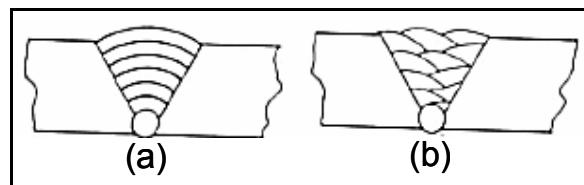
As técnicas de soldagem de (a) trançar e (b) filetar (Meyer, 2001).
